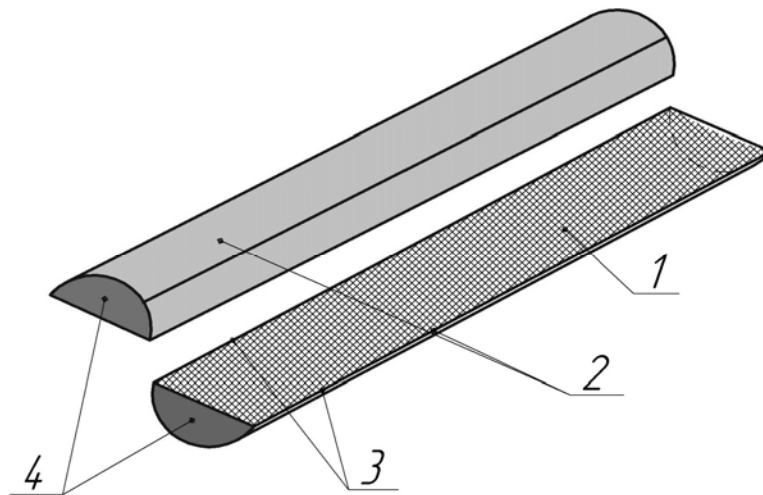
Конструкции патрона НРС для направленного разрушения горных пород
